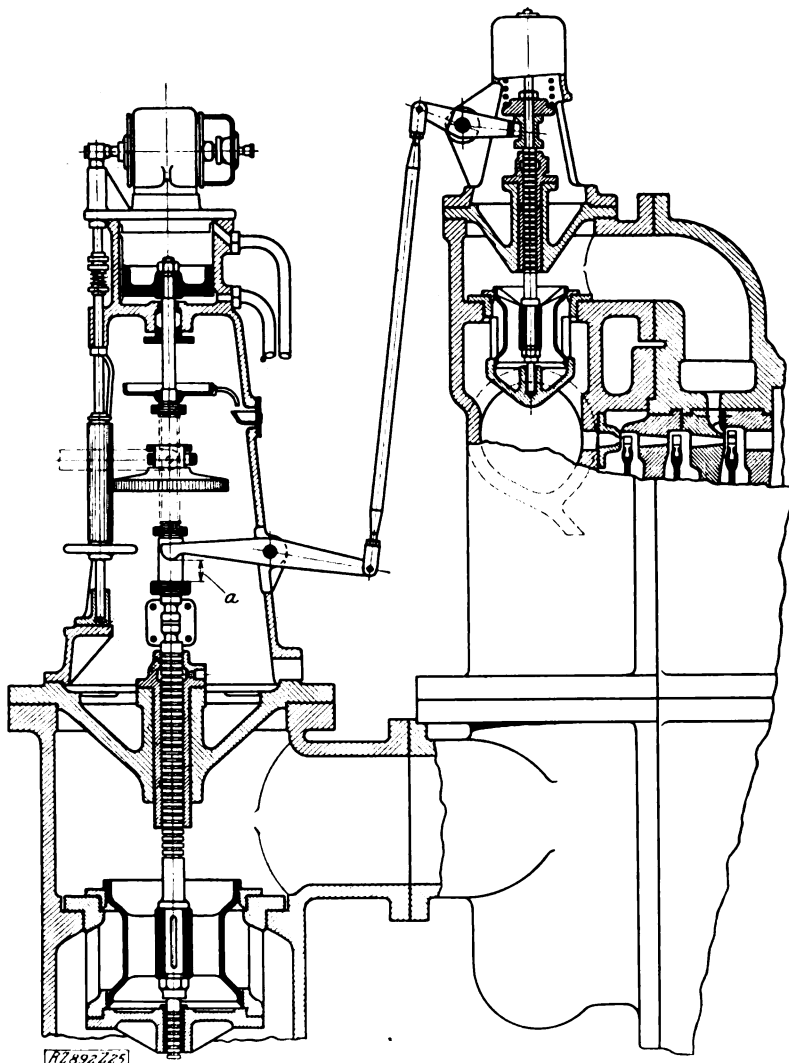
English Electric Co., Ltd., Steuerung mit Hauptdrosselventil und Überlastventil.
